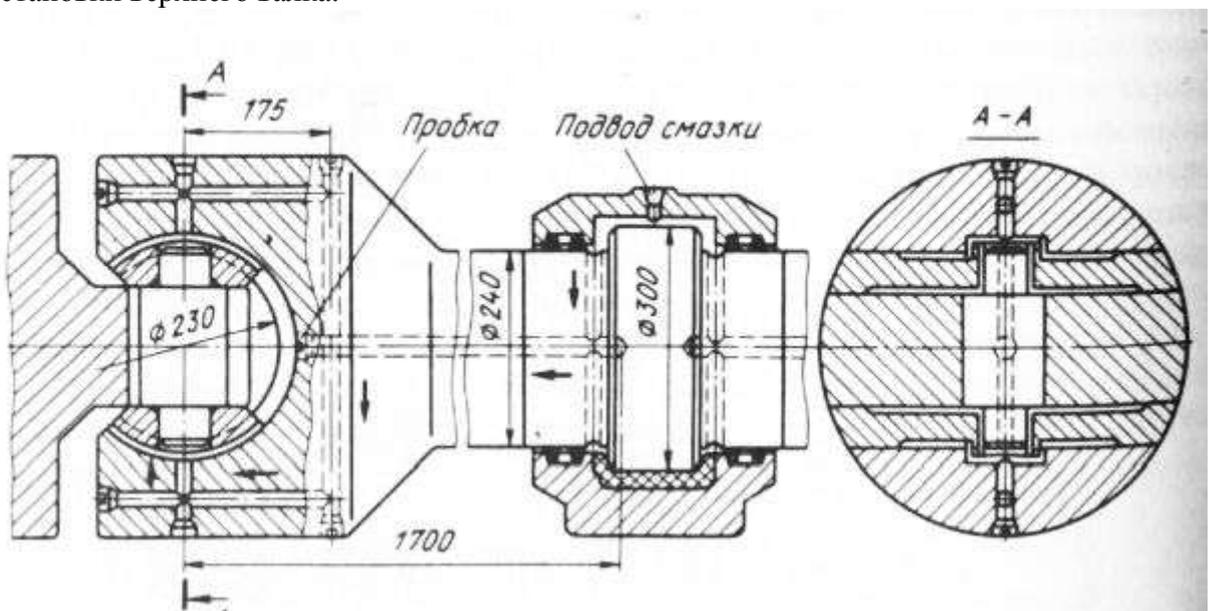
Универсальный шпиндель привода валков реверсивного стана 1700
